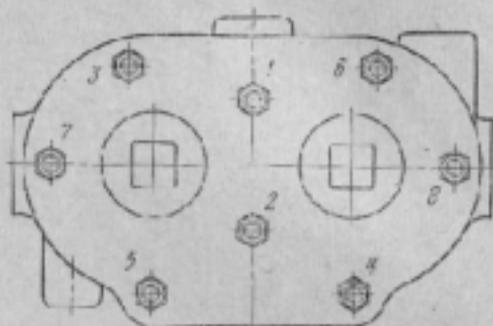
Порядок затягивания гаек штифтов крепления гайки цилиндров компрессора
